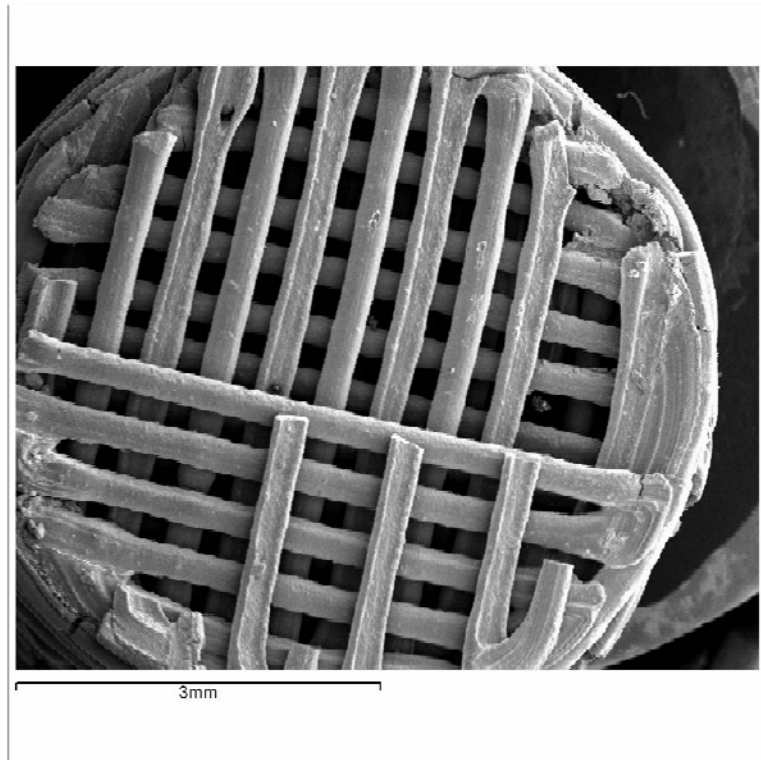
Vista SEM del plano superior de la pieza.
